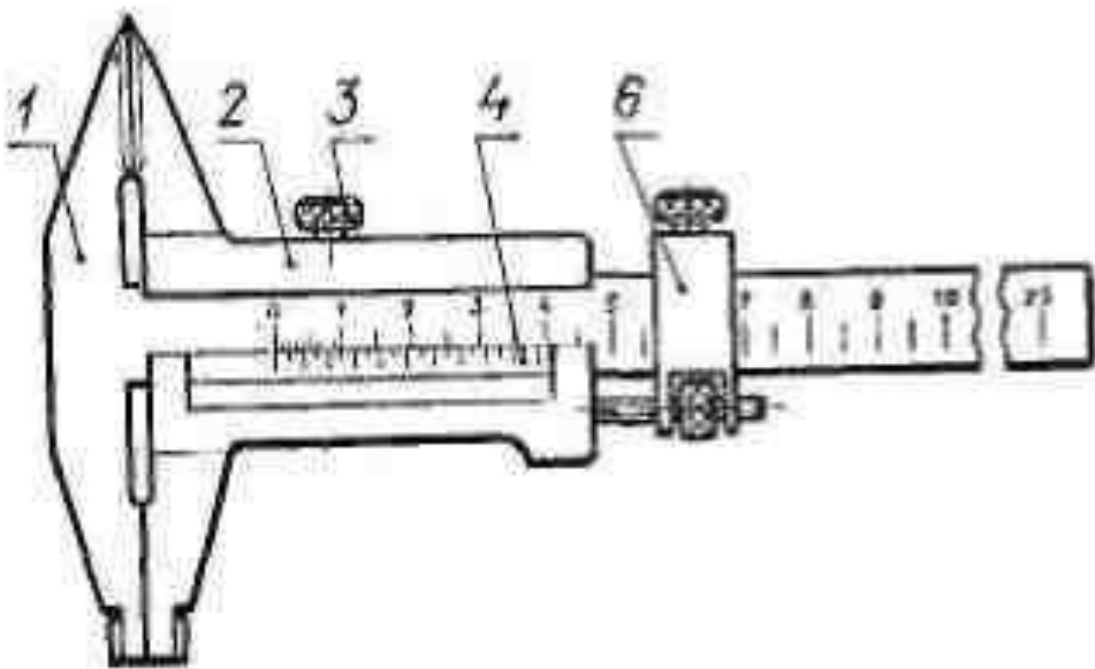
Штангенциркуль ШЦ-II: 1 – штанга; 2 – рамка; 3 – затискувач рамки; 4 – ноніус; 6 – рамка з мікрометричною подачею
